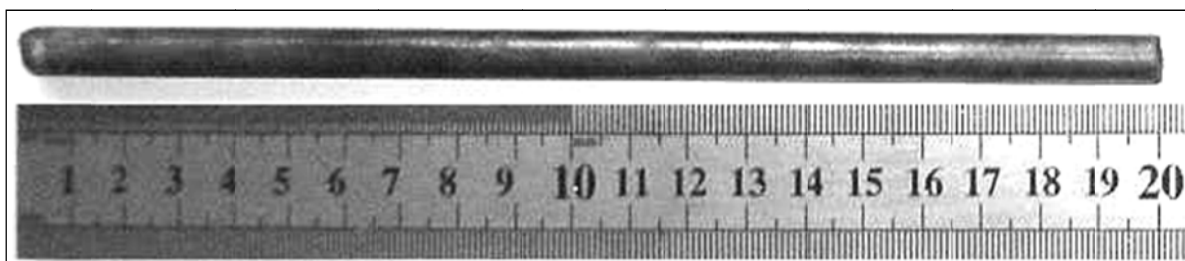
Типичный внешний вид стальной отливки малого сечения ( $\varnothing$  6,4 мм).
